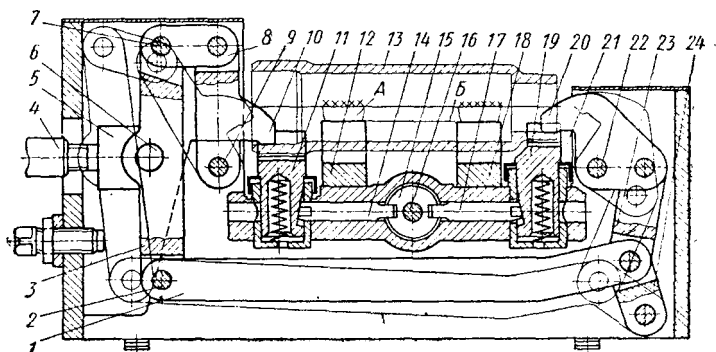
Двухместное фрезерное приспособление с рычажным усилителем и дополнительными опорами
